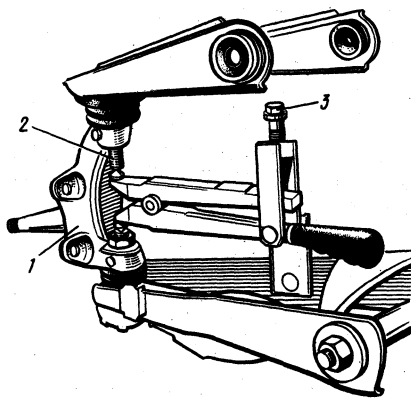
Выпрессовка пальца верхнего шарового шарнира автомобиля «Жигули»:
